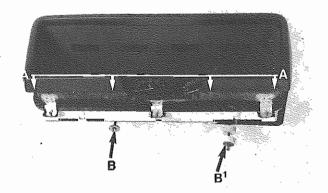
A - Viti fissaggio posteriore Rear screws
